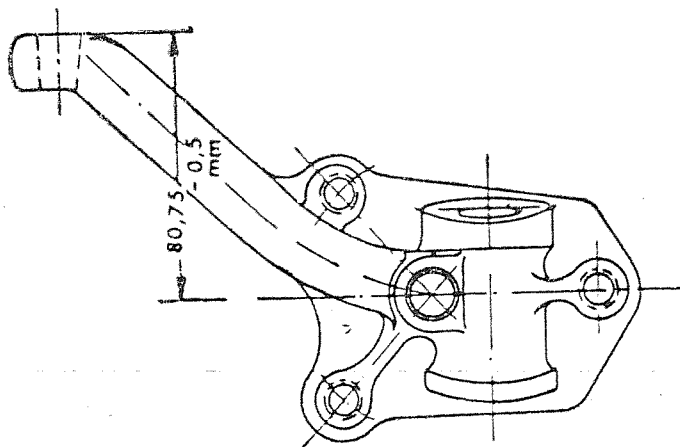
Punta de eje izquierda (la medida de la altura debe ser respetada).
